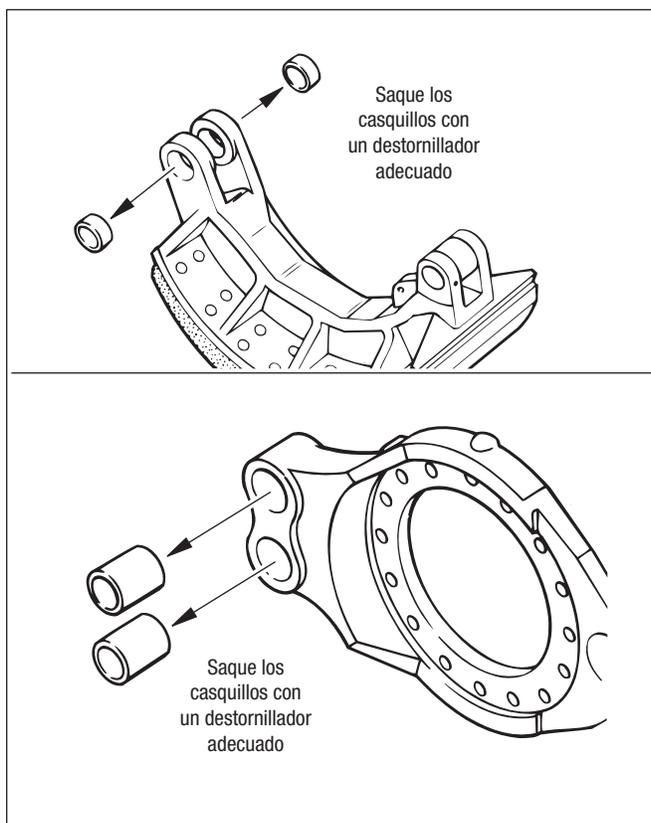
Desmontaje de casquillo de pasador de anclaje
